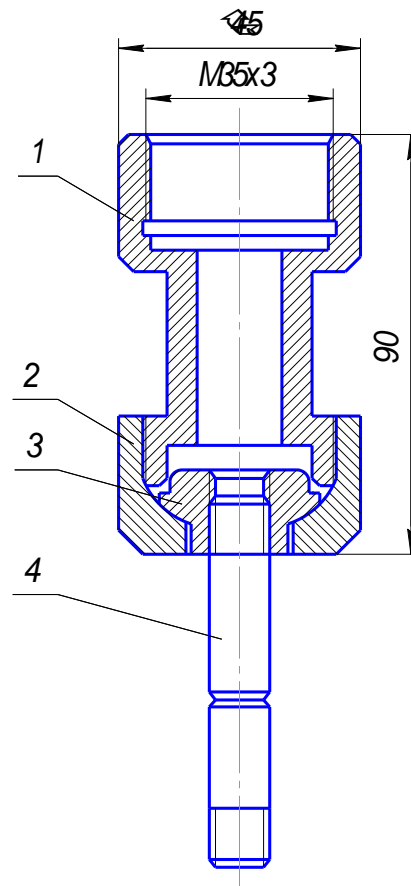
Захоплювач для закріплення металевого циліндричного зразка з кільцевою тріщиною: 1 – корпус захоплювача; 2 – гайка сферична; 3 – сухарик сферичний; 4 – циліндричний випробувальний зразок.
